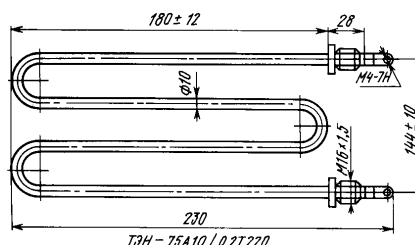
Габаритные, установочные и присоединительные размеры ТЭНа 75А10/0,2Т220
